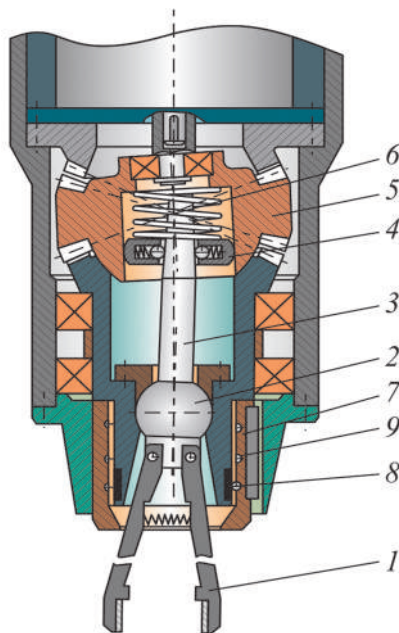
Mecanism precesional de apucare a robotului [28].
